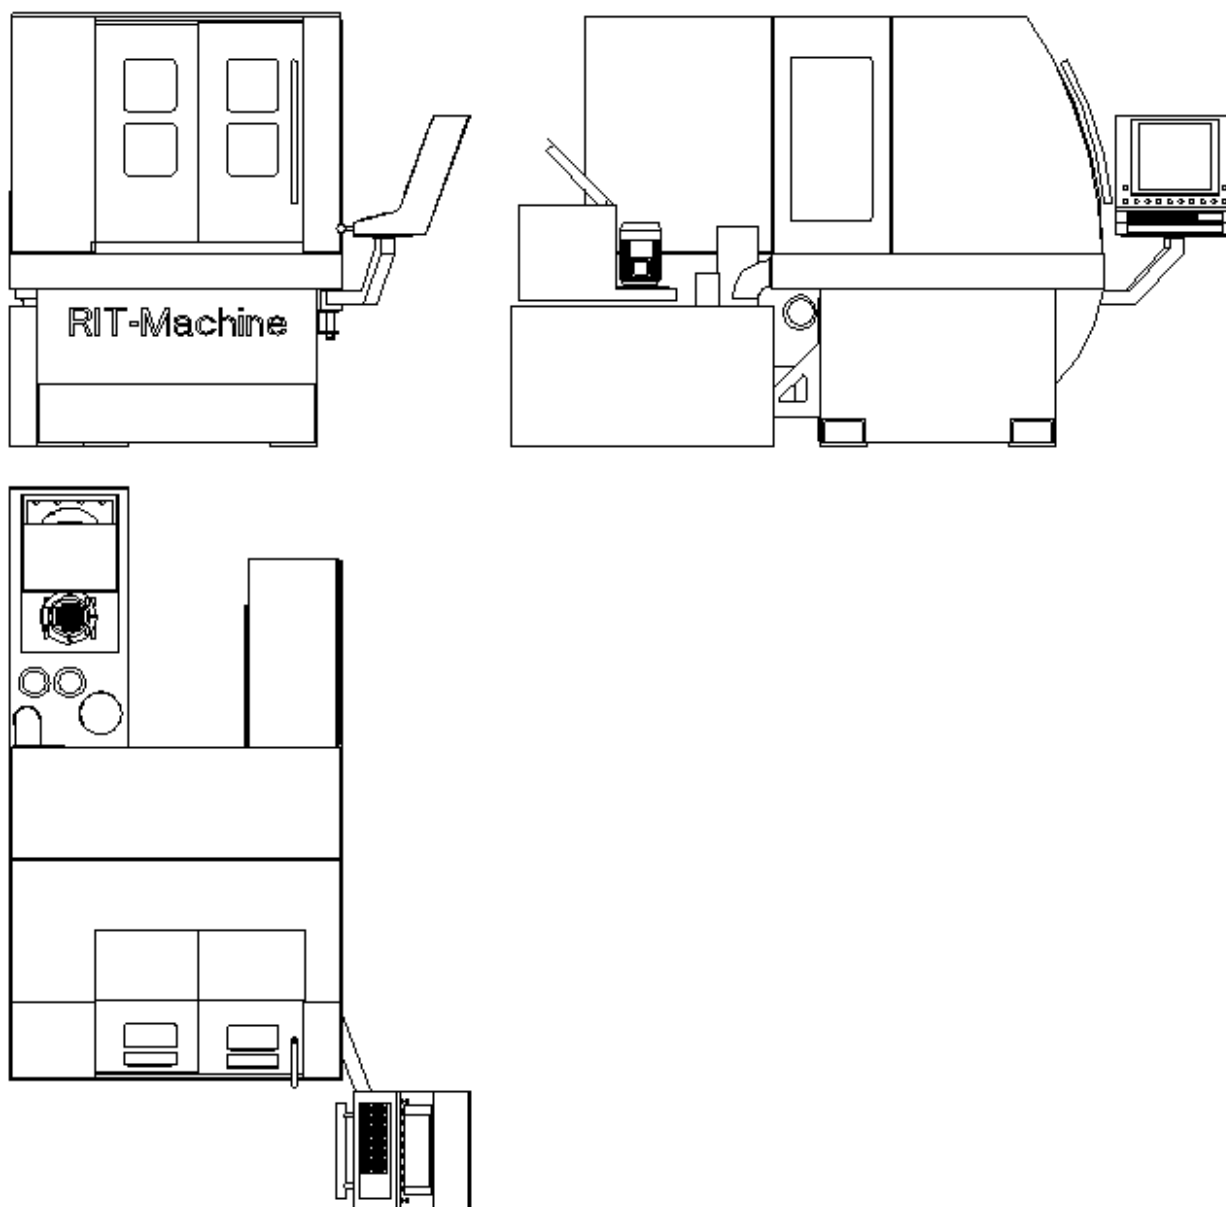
Общий вид базового исполнения шлифовально-заточного станка.
